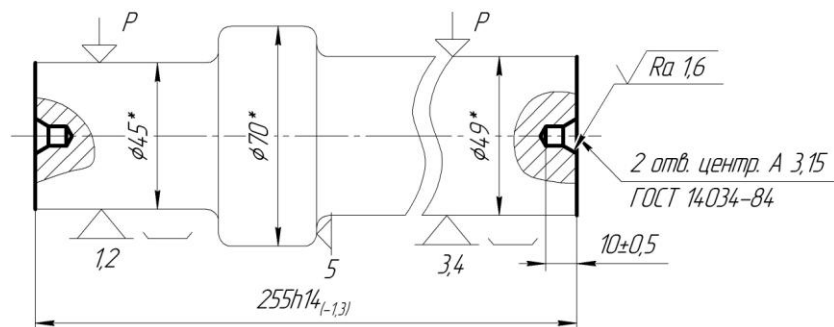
Схема базування заготовки в пристосуванні
